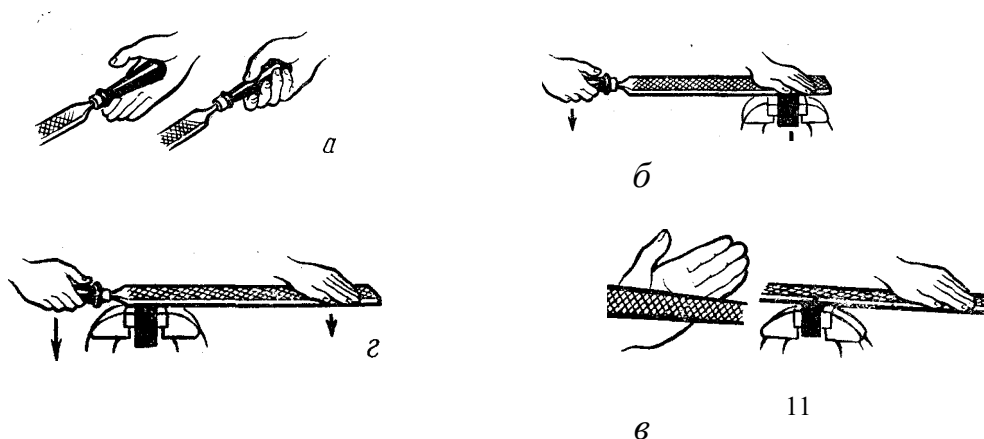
Хватка напильника и балансировка им в процессе опиливании: а — хватка правой рукой; б — хватка левой рукой; в — силы нажима в начале движения; г — силы нажима в конце движения.
